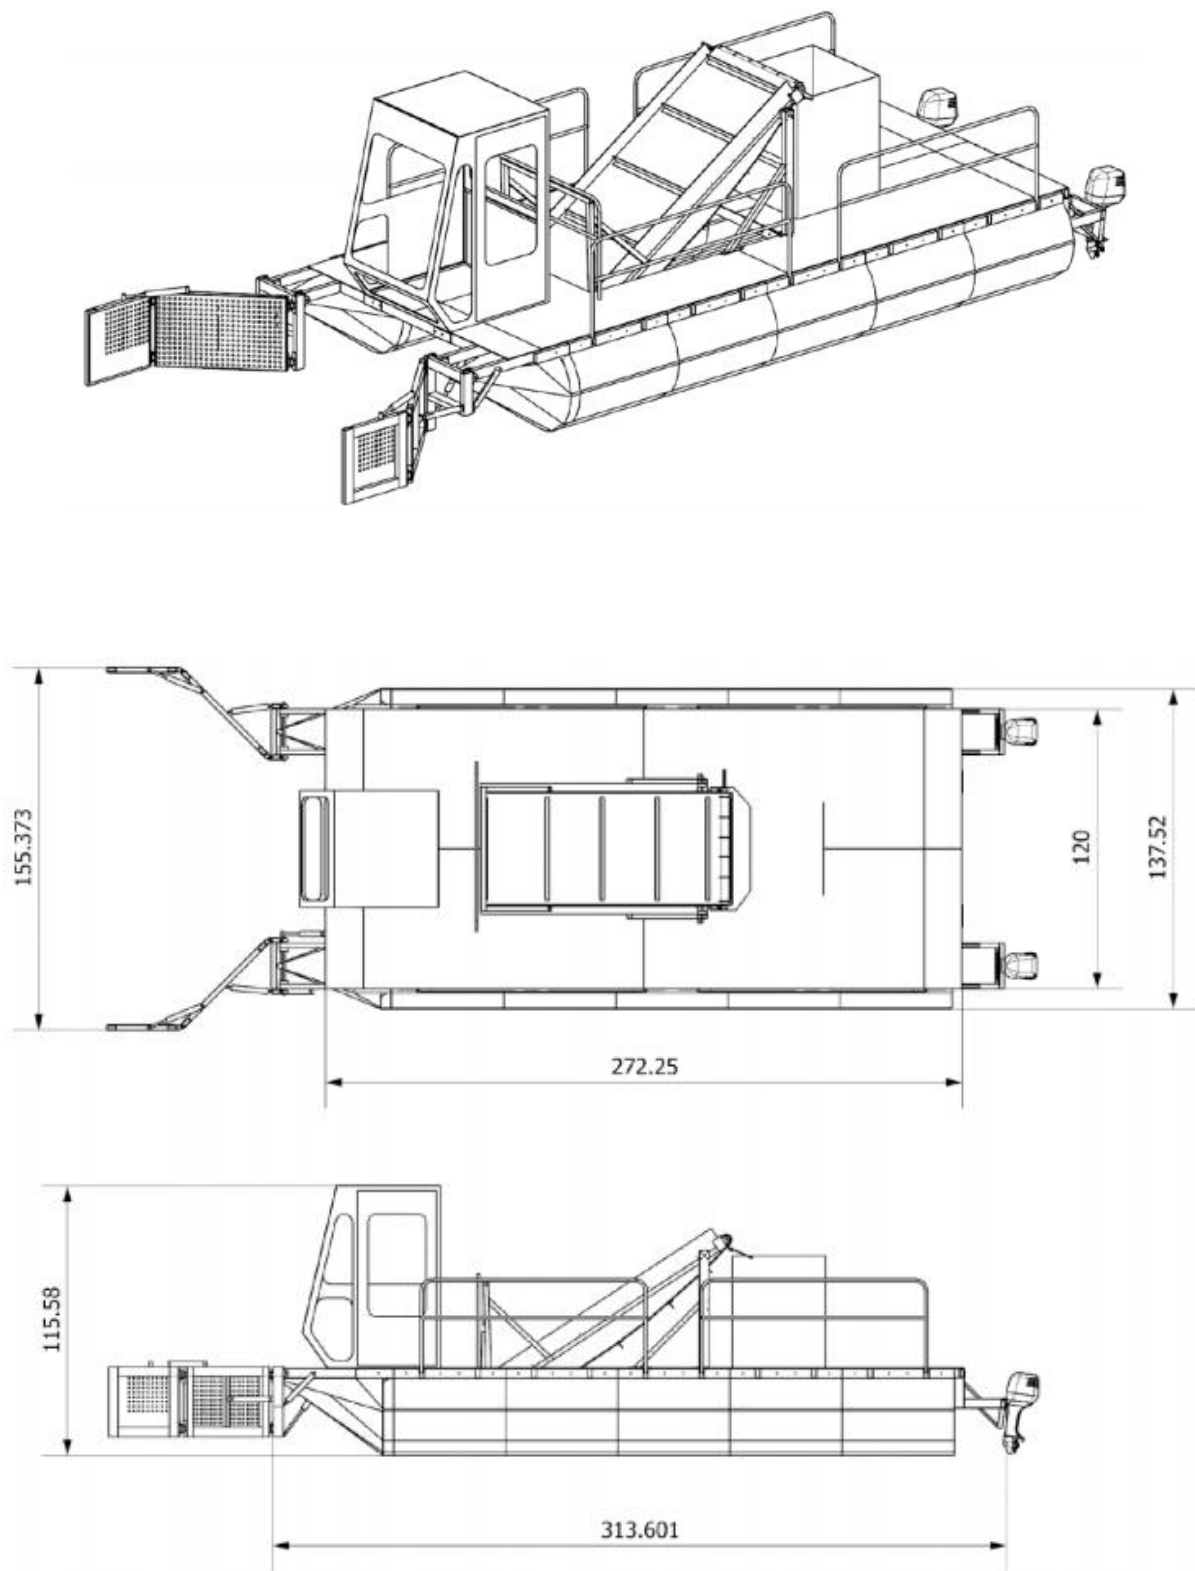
Dimensions del *Mobile Skimmer* (cm) (1)
